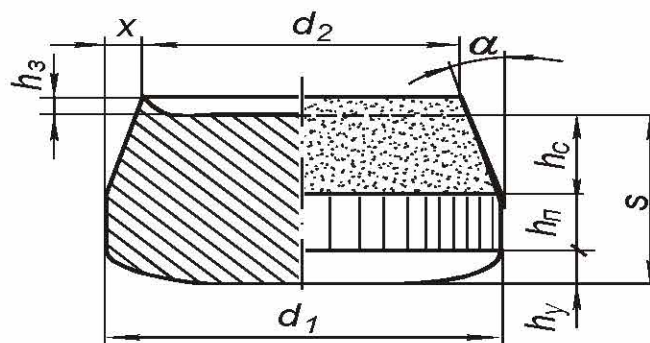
Дефекти бічної поверхні штампованої деталі
